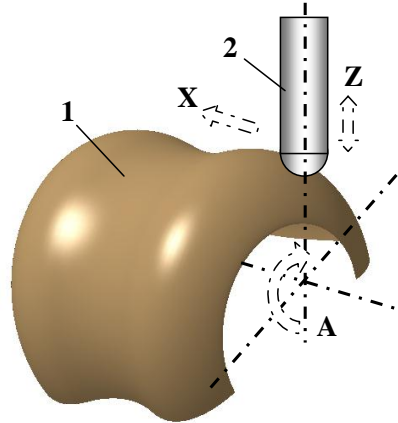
Схема формоутворення 3D поверхні на вертикально-фрезерному верстаті з ЧПК
